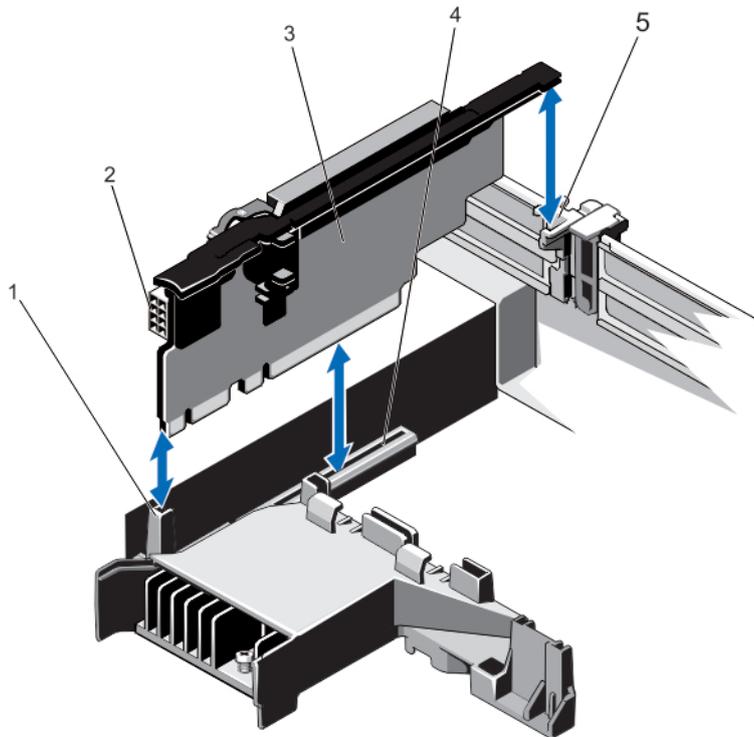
Extracción e instalación del soporte vertical 2 para tarjetas de expansión
